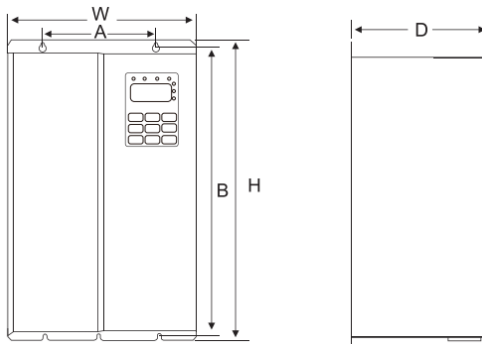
Внешний вид и размеры ПЧ (≥ 30 кВт)
